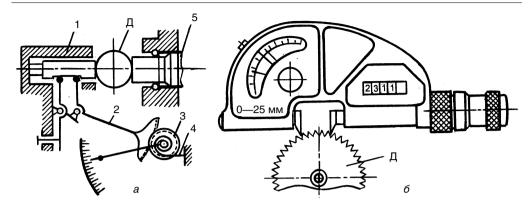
Рычажно-зубчатый инструмент: а — схема рычажной скобы (микрометра); б — скоба с цифровым отсчётом
